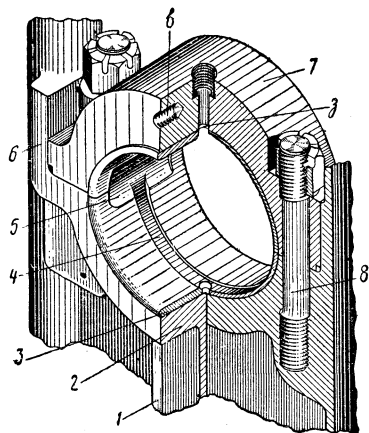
Коренной подшипник коленчатого вала дизеля 2Д50:
